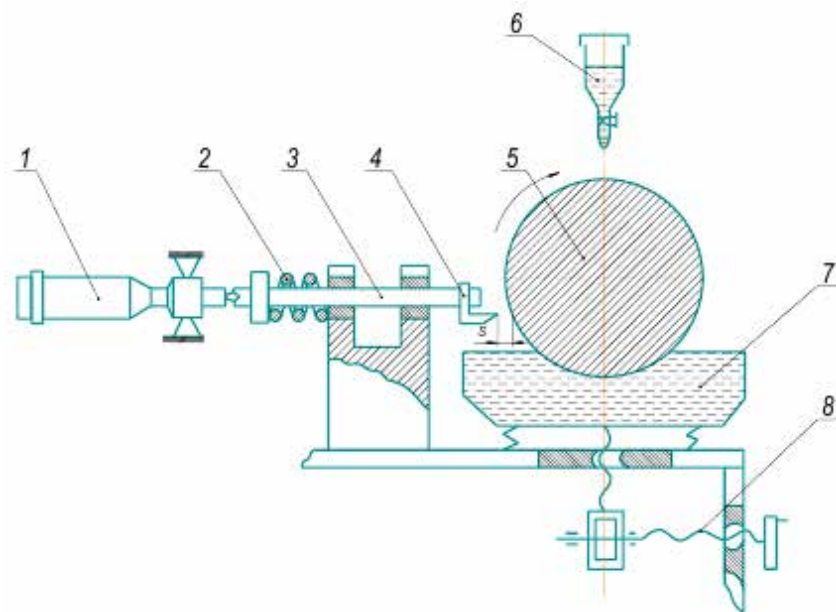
Схема установки для нанесення покриттів із розчинів полімерів методом занурення та заливки: 1 - мікрометрична головка; 2 - пружина; 3 - стрижень; 4 - ракель; 5 - деталь; 6 - резервуар; 7 - ванна; 8 - гвинтовий механізм; S - зазор між ракелем і деталлю.
